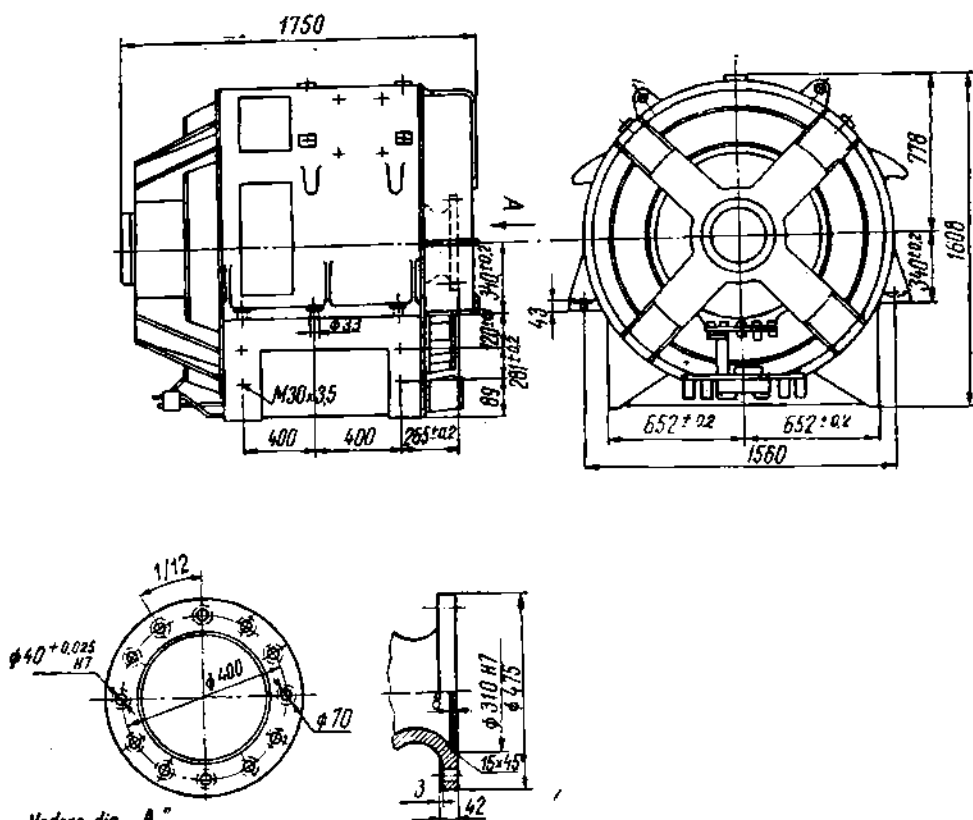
Generator principal tip GCE 1100/10 F și generator auxiliar tip GE 575/8 F.
